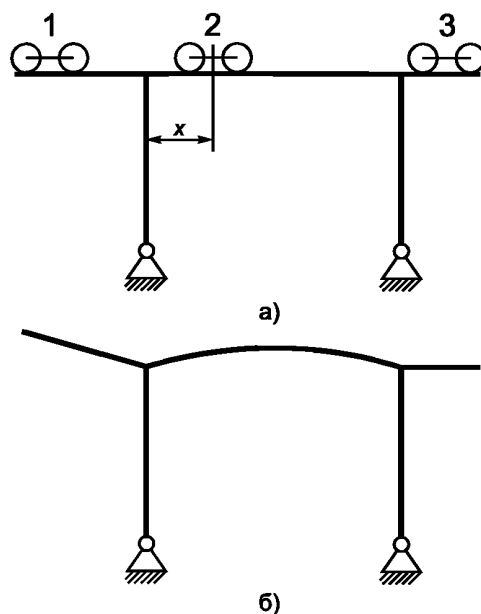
Схемы к определению параметров строительного подъема главных балок козлового крана
